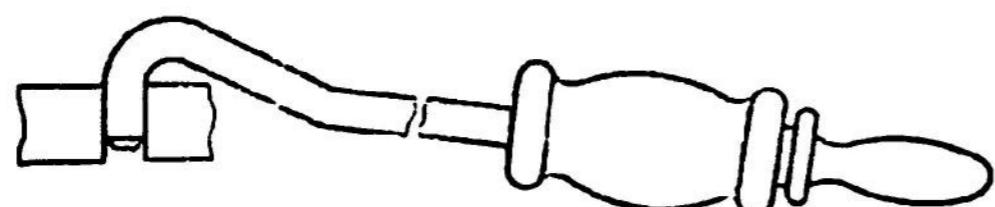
Съемник И801.18.000 крышек коренных опор коленчатого вала
